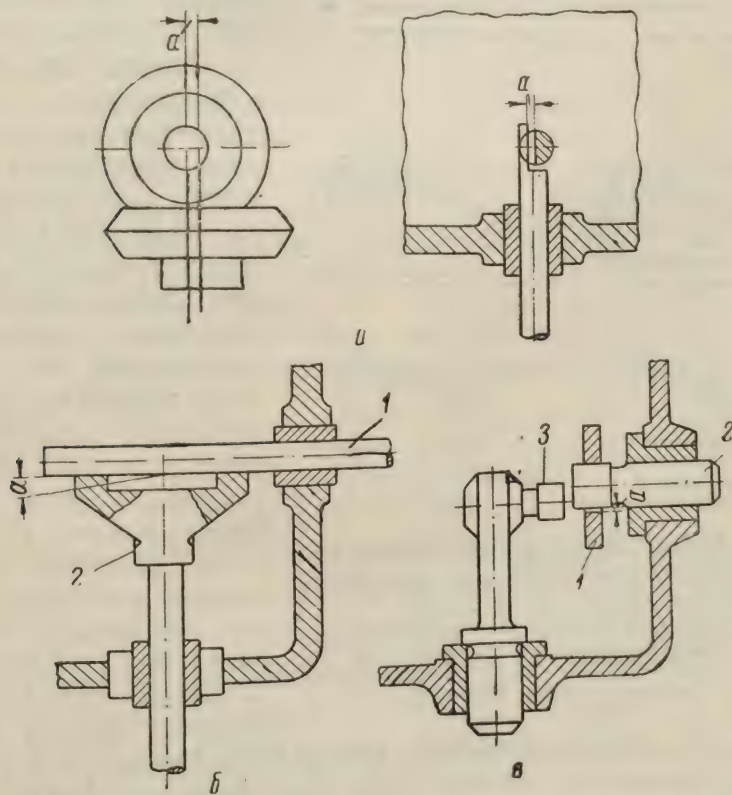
Проверка правильности установки конических колес: а—схема проверки пересечений осей в конической зубчатой передаче; б—схема проверки угла между осями зубчатых колес в конической передаче; в—проверка правильности взаимного расположения гнезд для осей конических колес.
